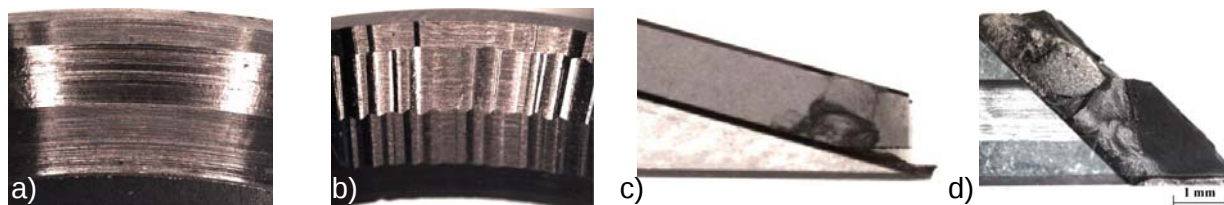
Geometria da sede de válvula e lâminas com fraturas, a) superfície correta usinada; b) erro de forma da superfície usinada; c) lâmina fraturada de 15° e d) lâmina fraturada de 45°
